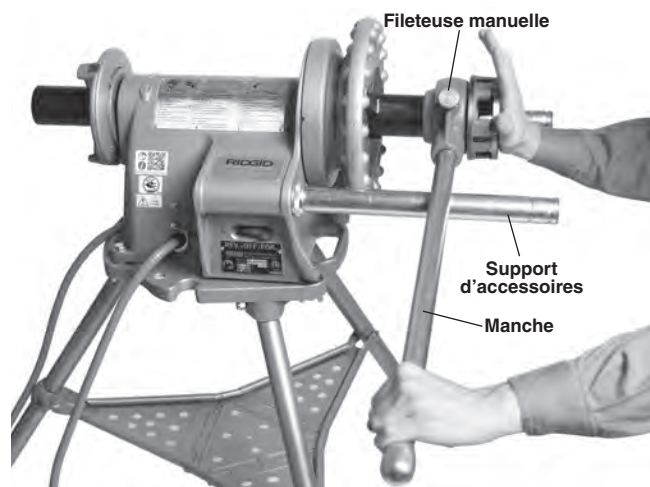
Enfoncement de la fileteuse sur le tuyau pour engager les filières
